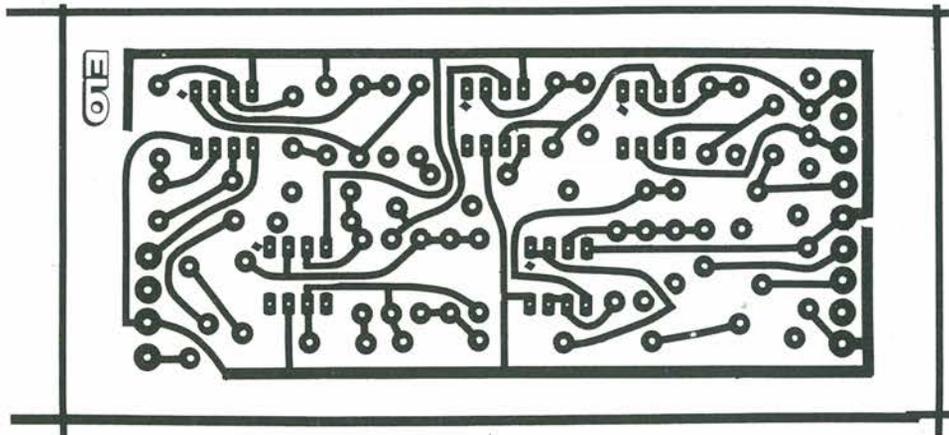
Circuito stampato scala 1:1 del Millivoltmetro.
